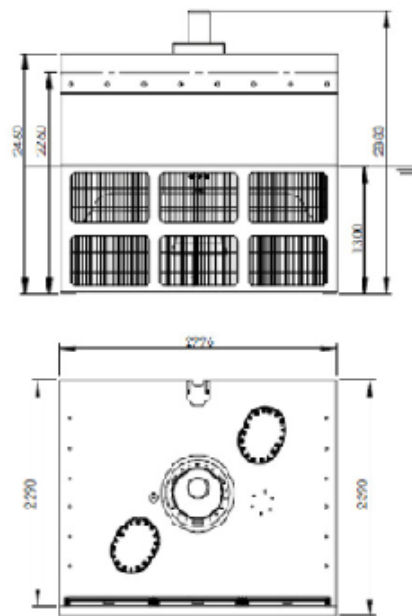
Módulo Drakoo B0004SP y dimensiones.
